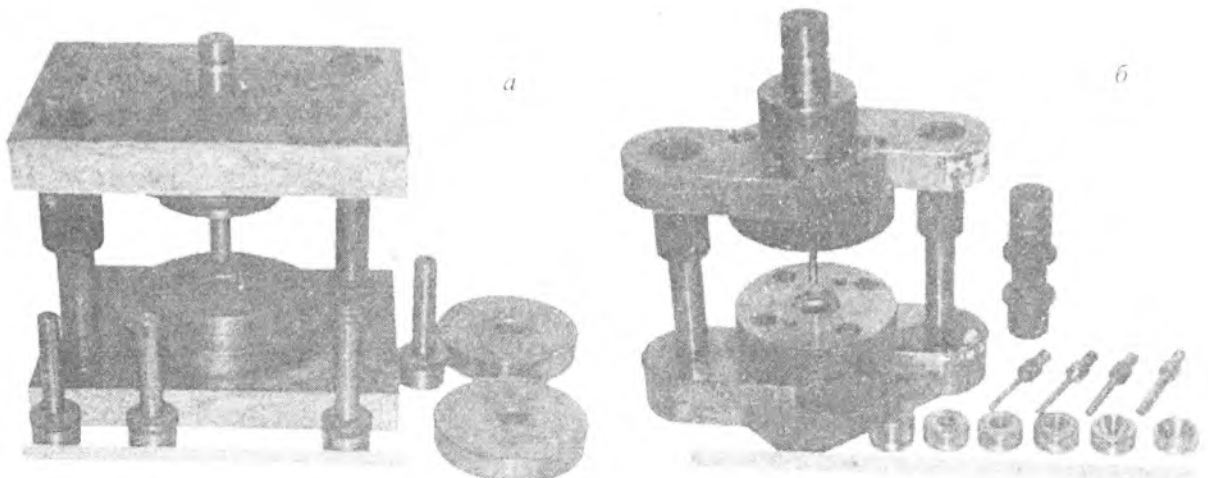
Общий вид штампов, матриц и пуансонов для совместной выгвозки металлической основы и металлопорошкового покрытия
